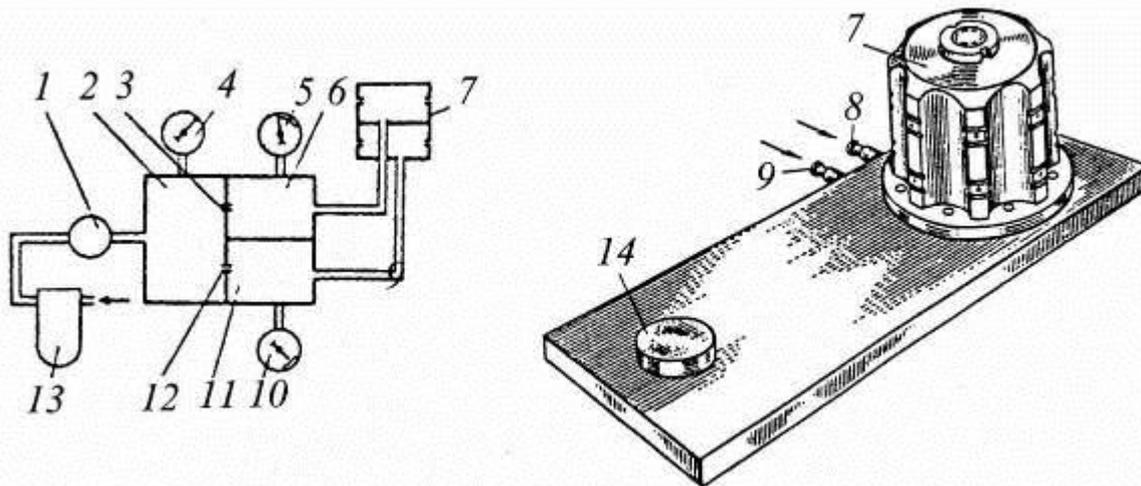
Пневматический прибор для измерения отверстий: 1 — стабилизатор давления; 2 — ресивер; 3, 12 — входные сопла; 4, 5, 10 — манометры; 6, 11 — камеры; 7 — пневматический калибр; 8, 9 — трубки; 13 — воздушный фильтр; 14 — грибок
